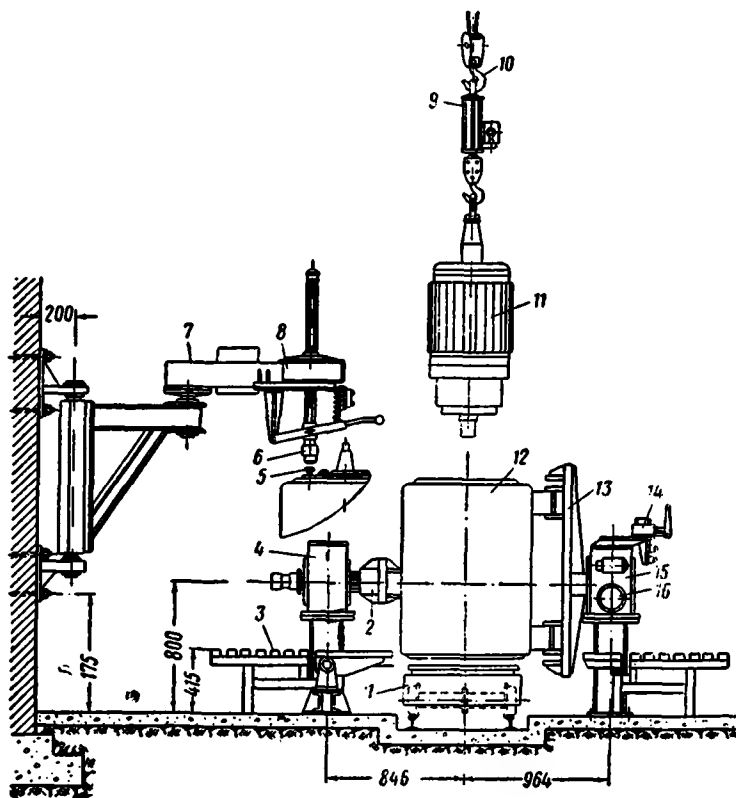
Рабочая позиция конвейера для сборки якоря с остовом тягового двигателя НБ-406 в кантователе:
